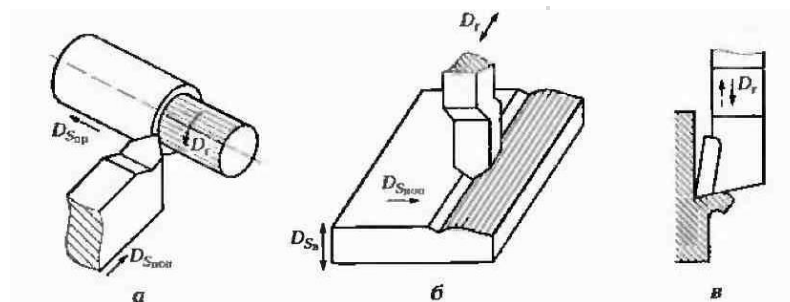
Токарный, строгальный (б) и долбежный (в) резцы:
